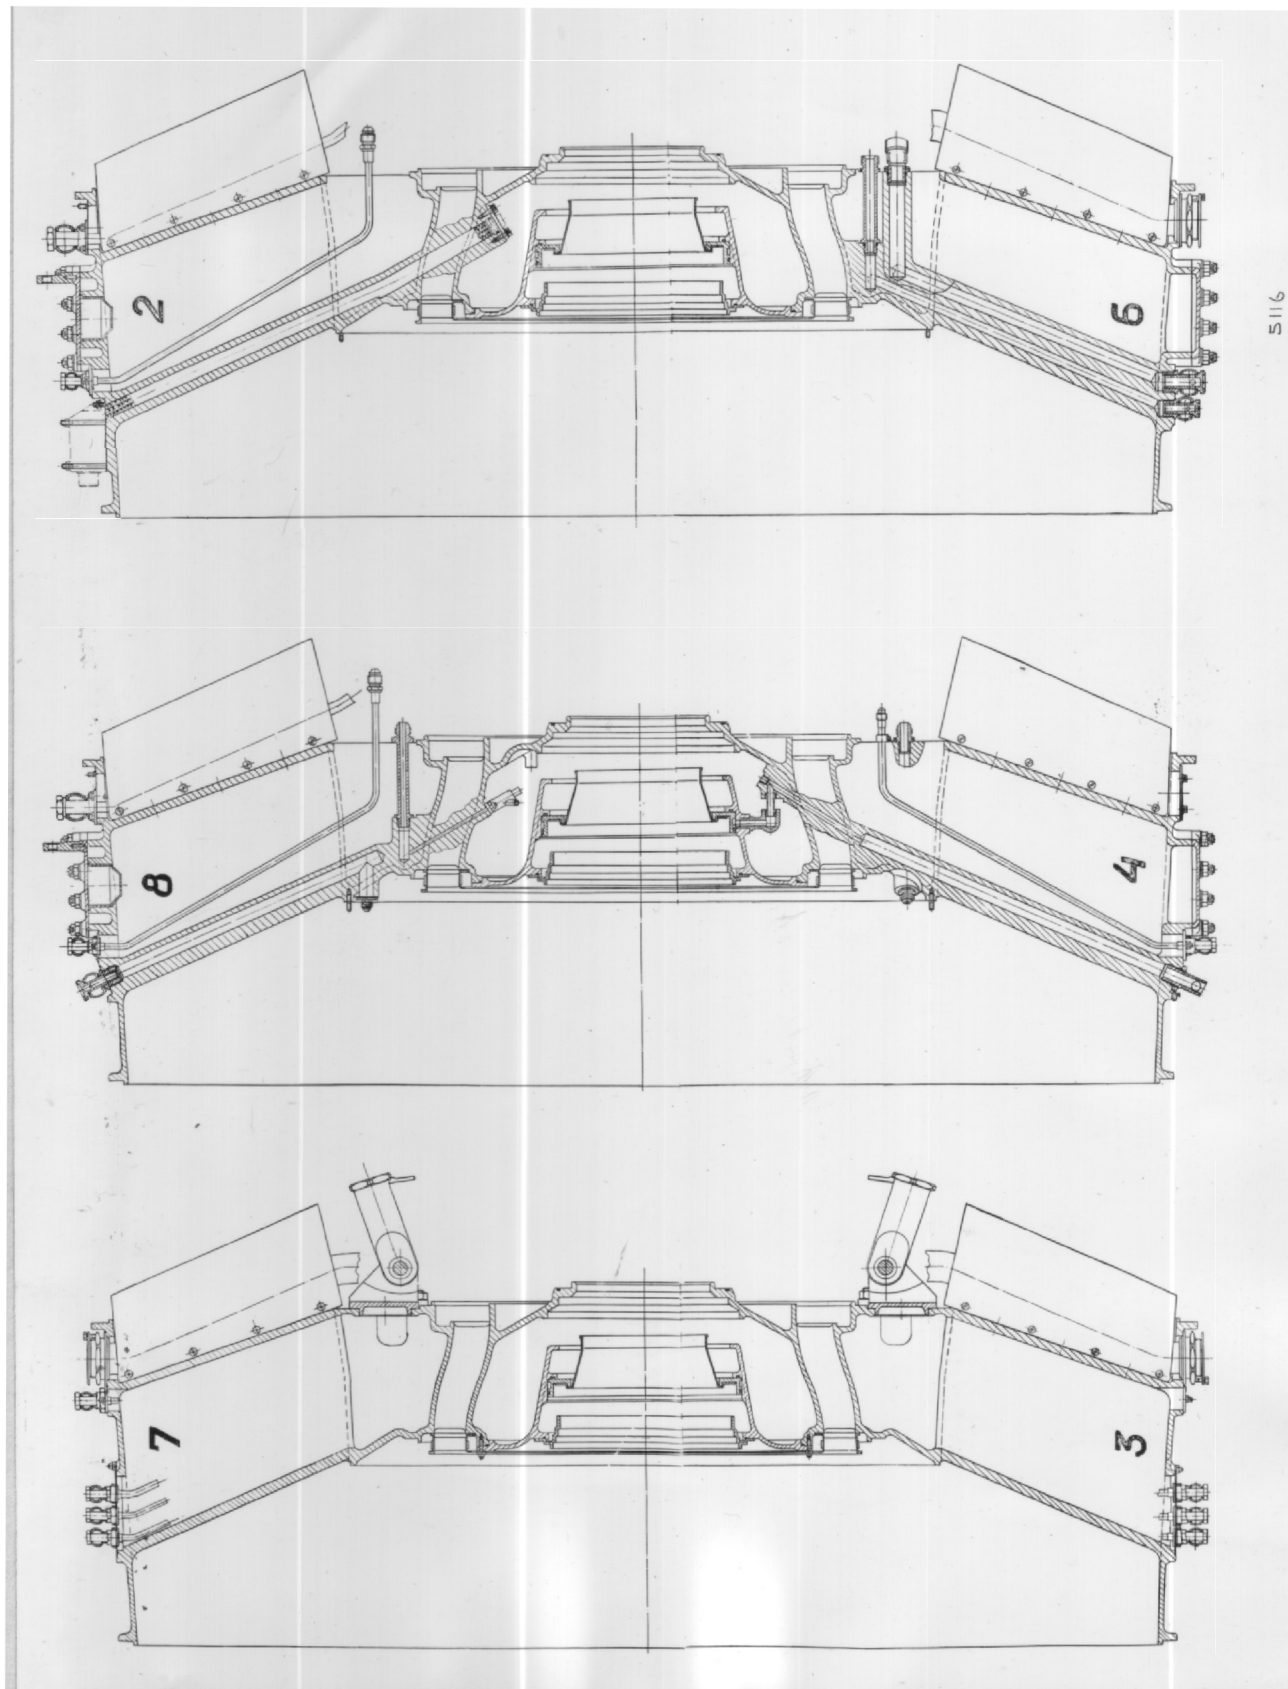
Промежуточный корпус (вид сзади)
